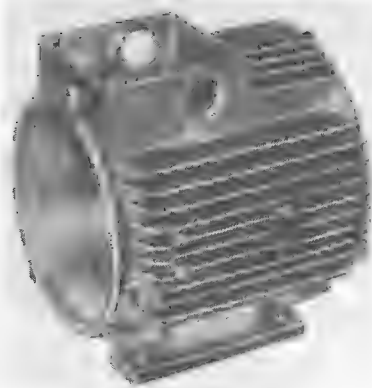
Станина двигателя из алюминиевого сплава с прилитыми коробкой выводов и лапами (высота оси вращения 80 мм)
